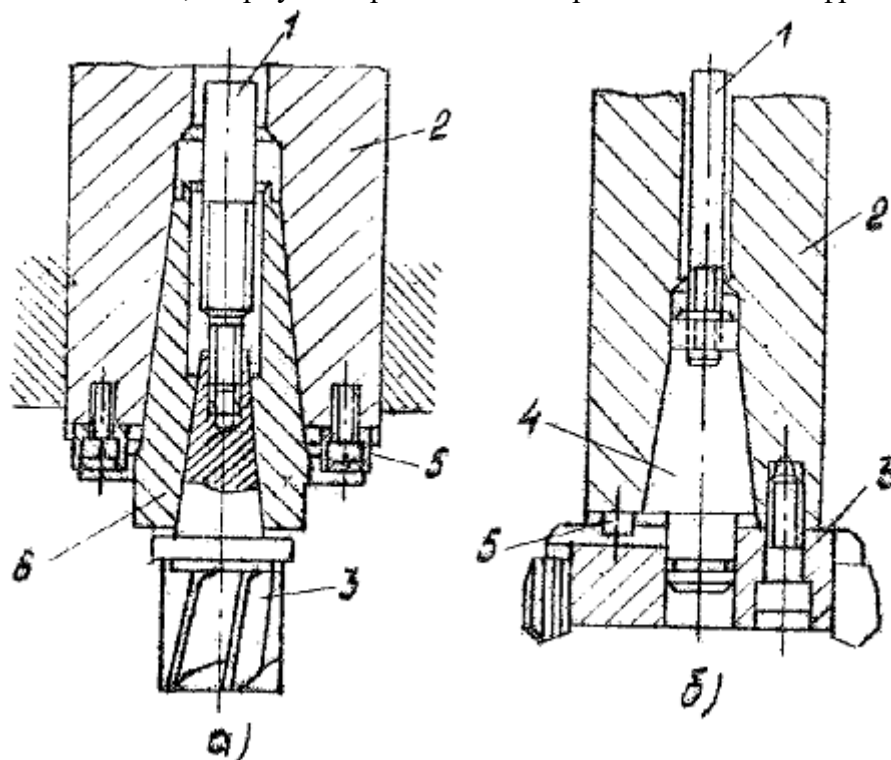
Крепление на станке фрез: а – с хвостовиком; б – с отверстием;
